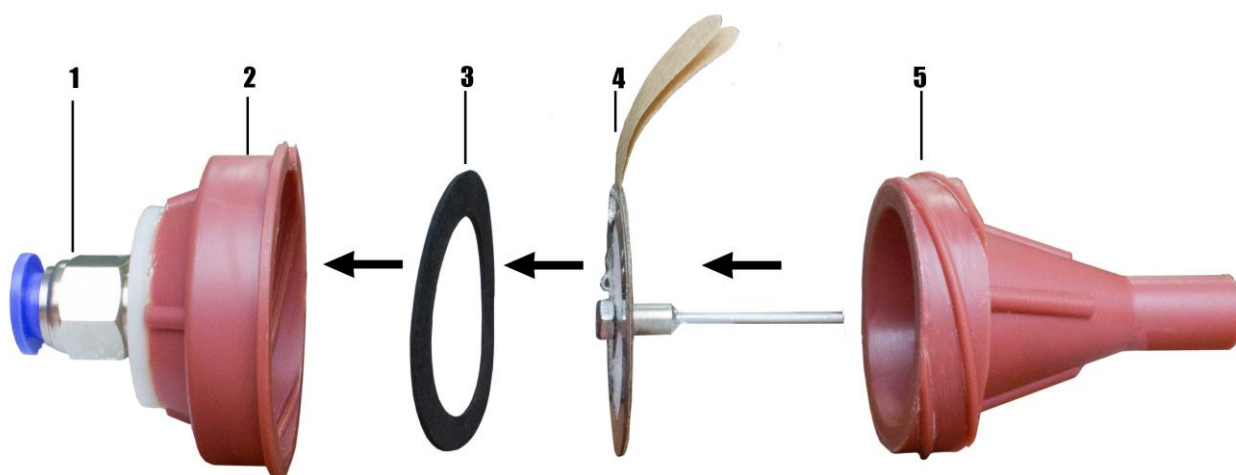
Схема сборки патрона-разбавителя пробы пыли
